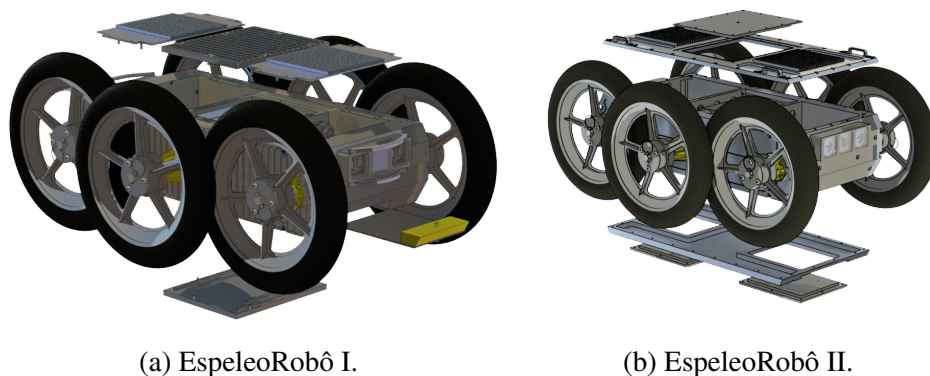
Vista explodida das tampas superior e inferior do EspeleoRobô versão I e II.
